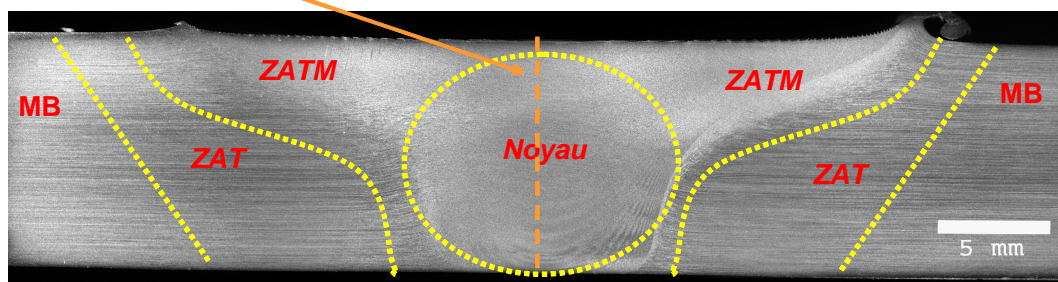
Macrographie d'une soudure FSW d'un alliage d'aluminium [5]
